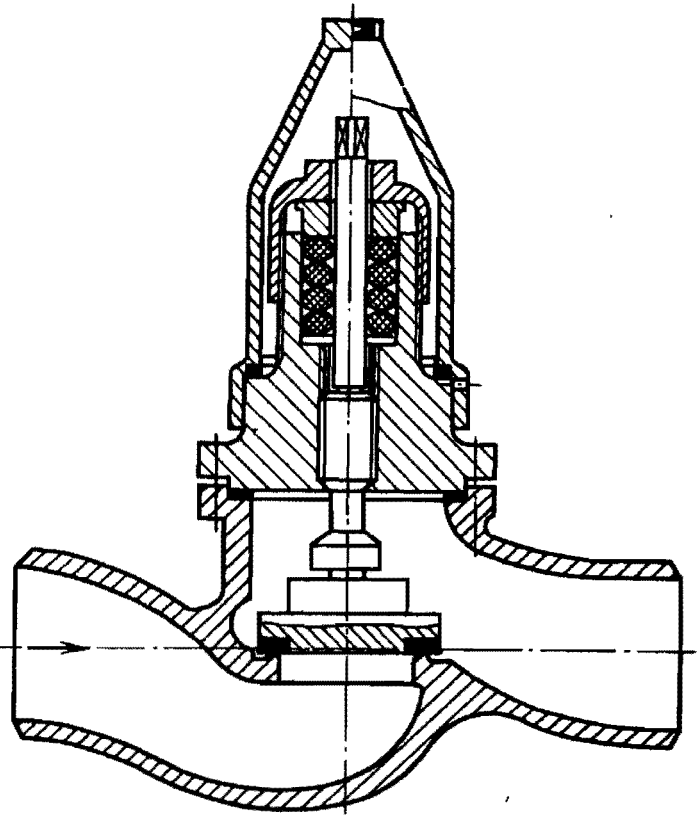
Запорный клапан с присоединением под приварку и защитным кожухом
